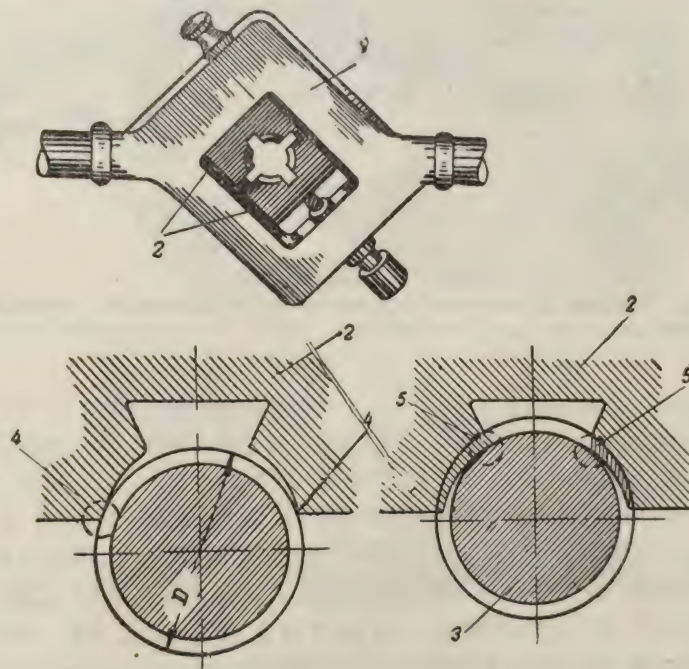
Раздвижная плашка, закрепленная в круппе:
